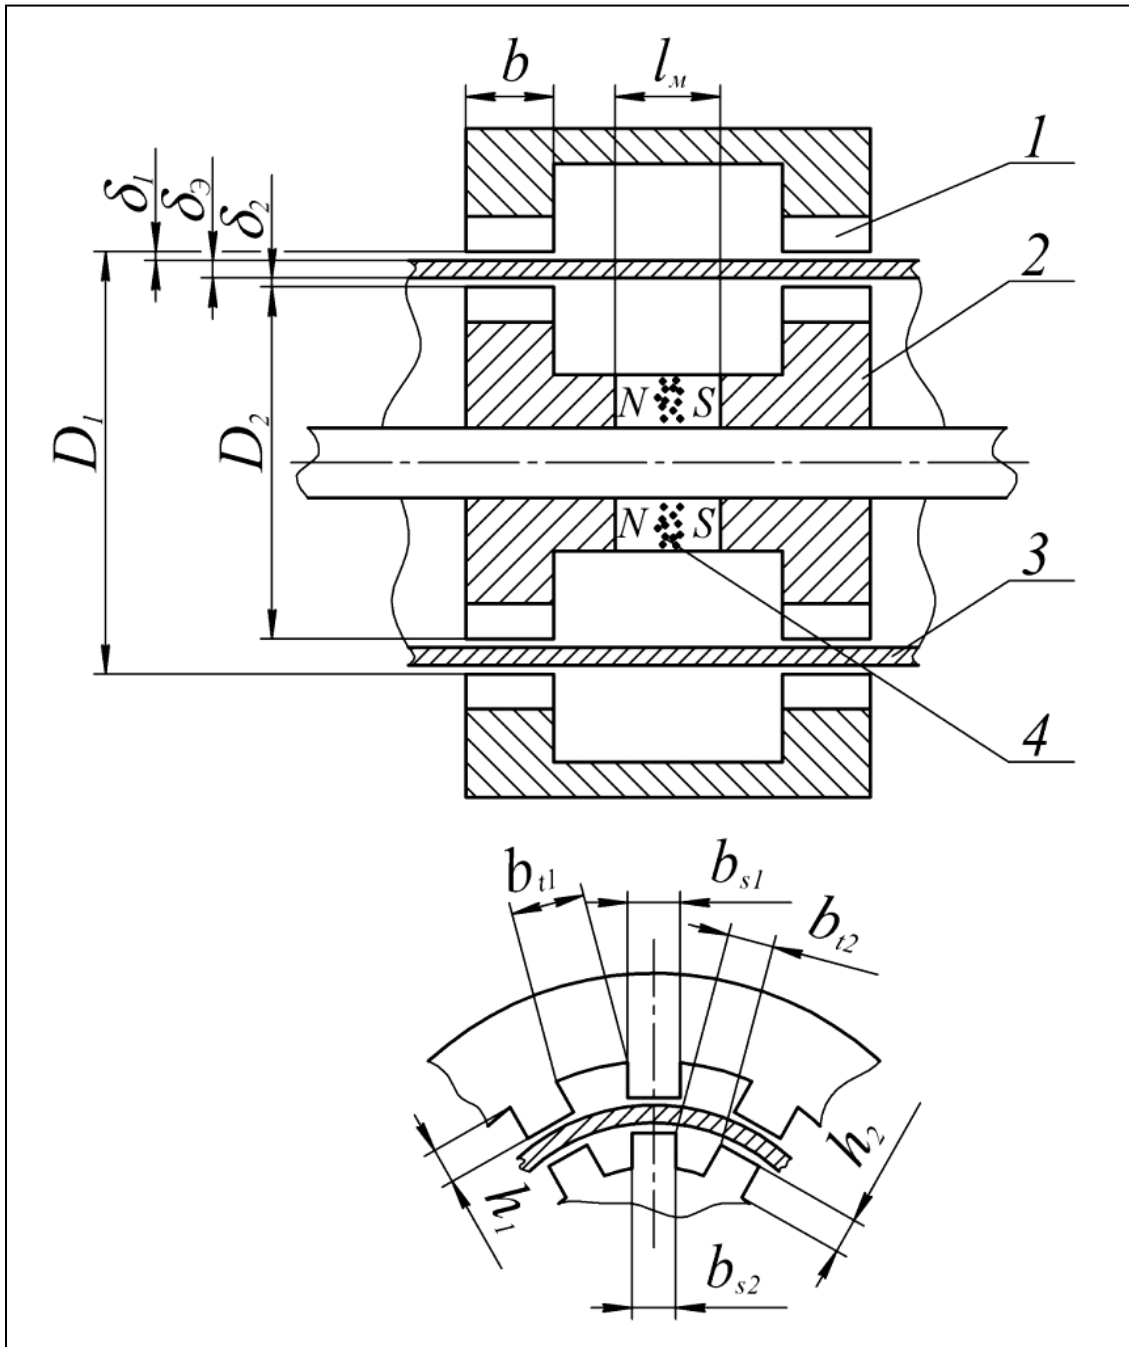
Вакуумная зубчатая передача с бесконтактным магнитным взаимодействием: 1 – внешнее зубчатое колесо; 2 – внутреннее зубчатое колесо; 3 – экран; 4 – магнит
